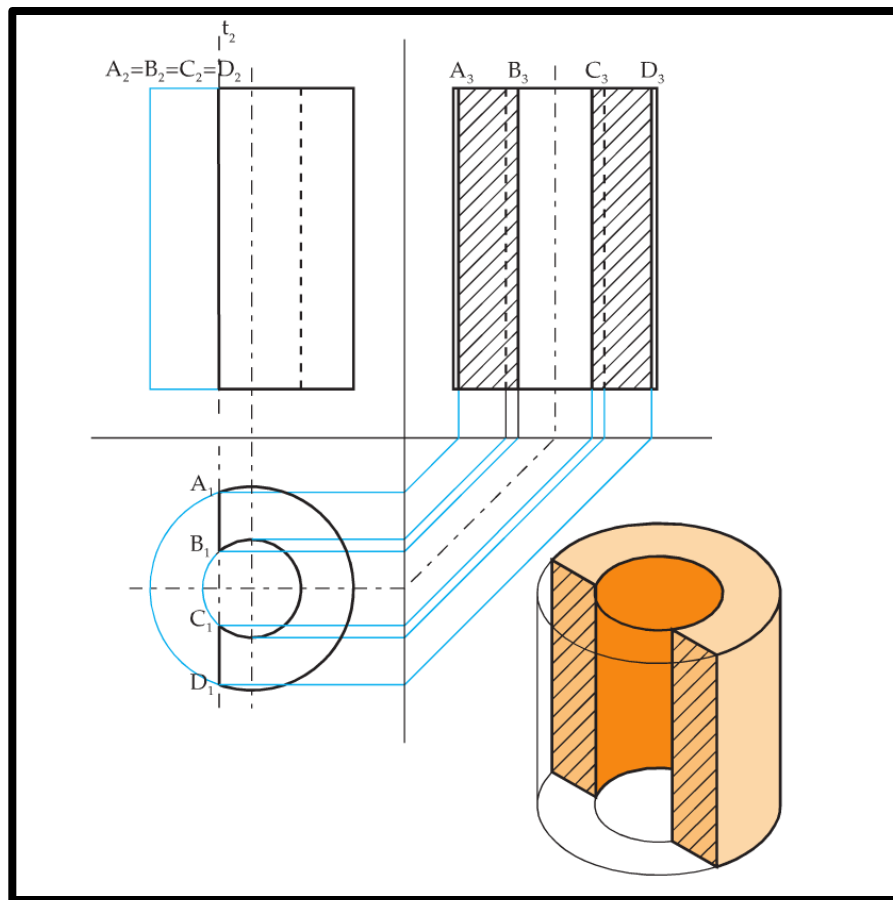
Sezione di un cilindro cavo con un piano t_2 parallelo all'asse
